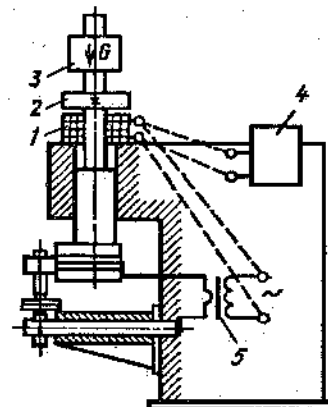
Схема электромагнитного механизма сжатия деталей при точечной сварке
